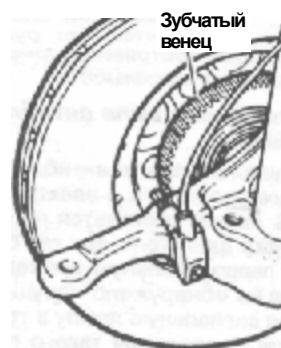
Колесный датчик и зубчатый венец в сборе — тормозная система ABS
